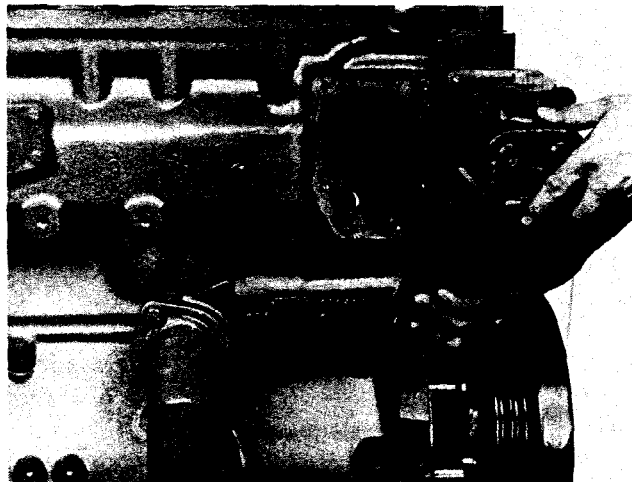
, (N100142). Remoción del conjunto de entrada de agua.
